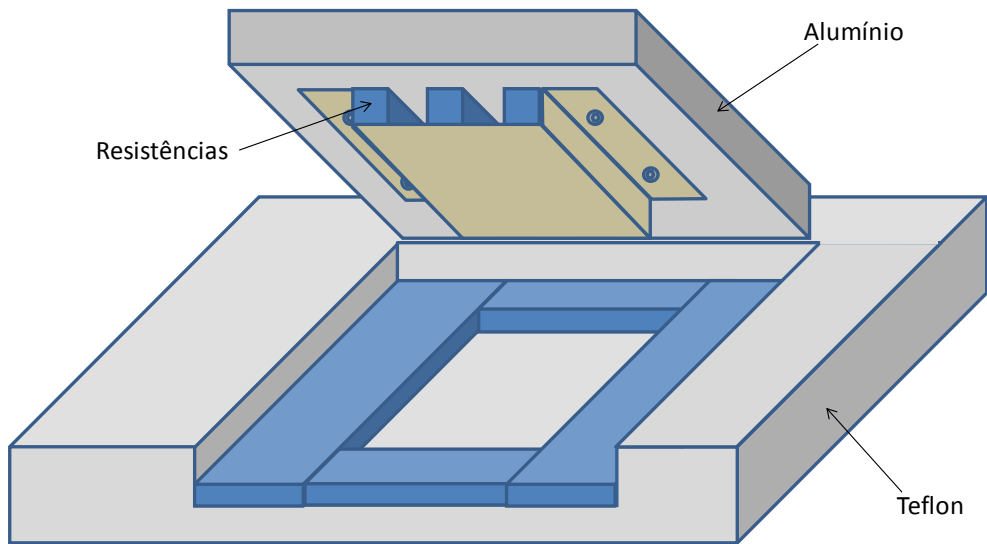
Montagem do conjunto - chapa de alumínio, resistências, suporte em teflon.
